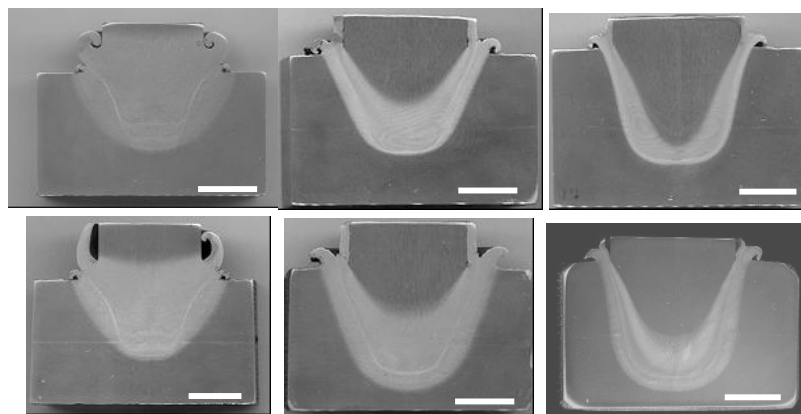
Arranjo de imagens macroscópicas das amostras obtidas com o processo de soldagem.
